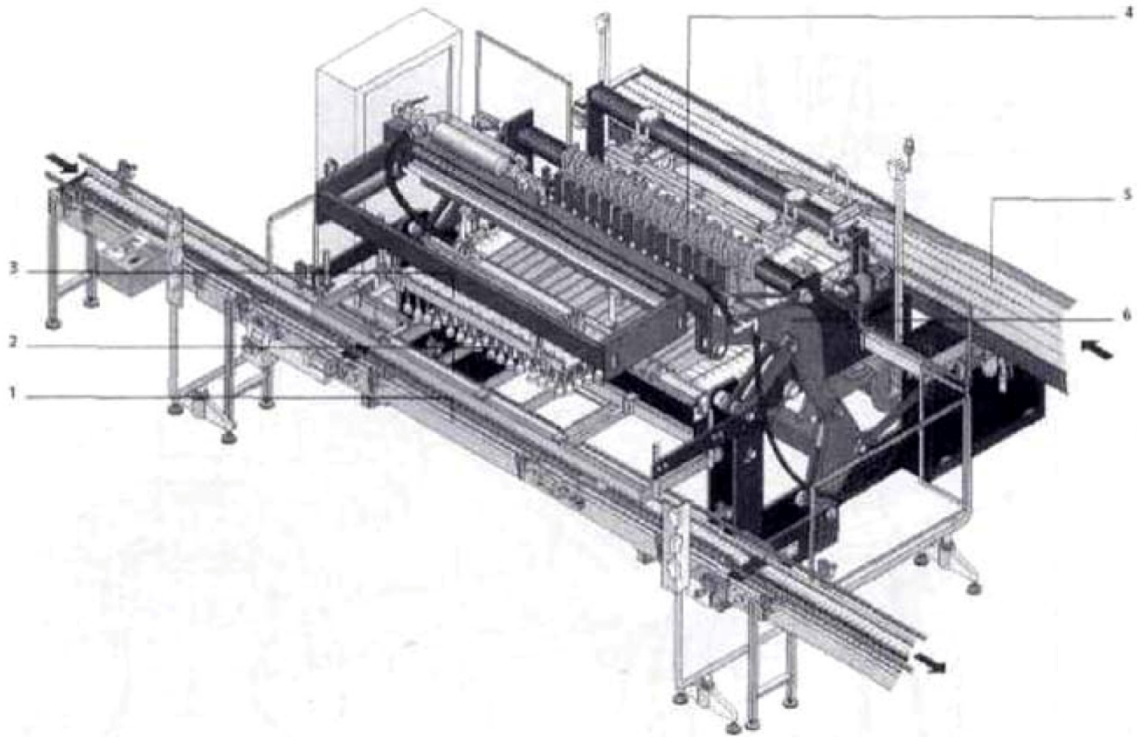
Завантажувач з переривчастим рухом типу «Innopack Garant GT»: 1 – транспортування упаковки, 2 – центрувальна рама, 3 – захватна головка, 4 – розподільувач пляшок, 5 – подача пляшок або банок, 6 – приводний механізм
